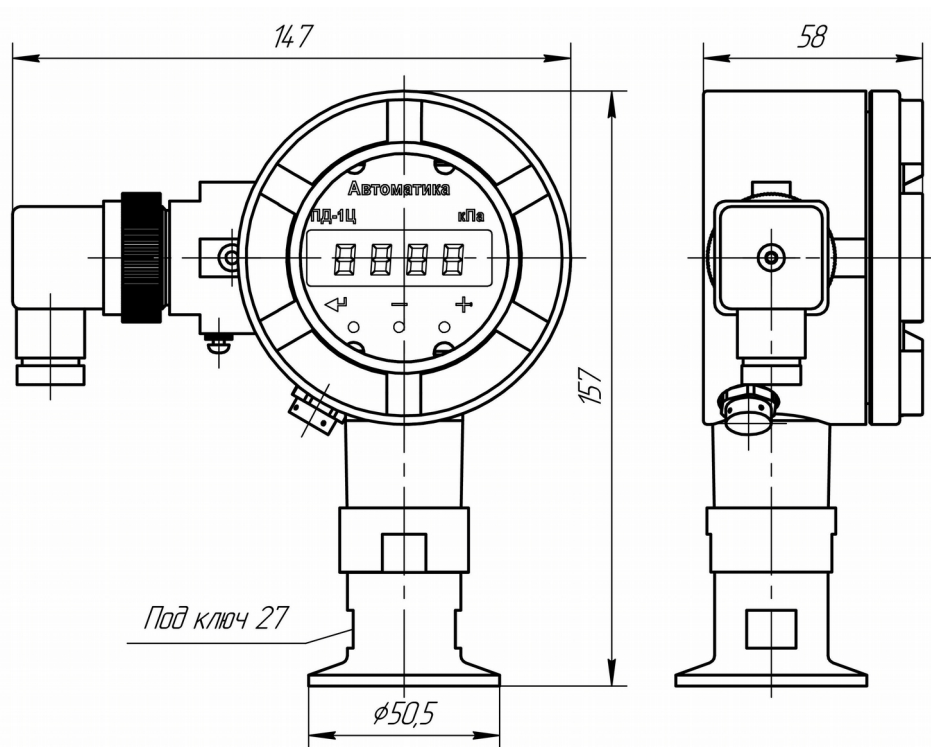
Габаритные и монтажные размеры ПД-1ЦМ с открытой мембраной из нержавеющей стали под кламп (Tri-clamp DN=1 1/2")
